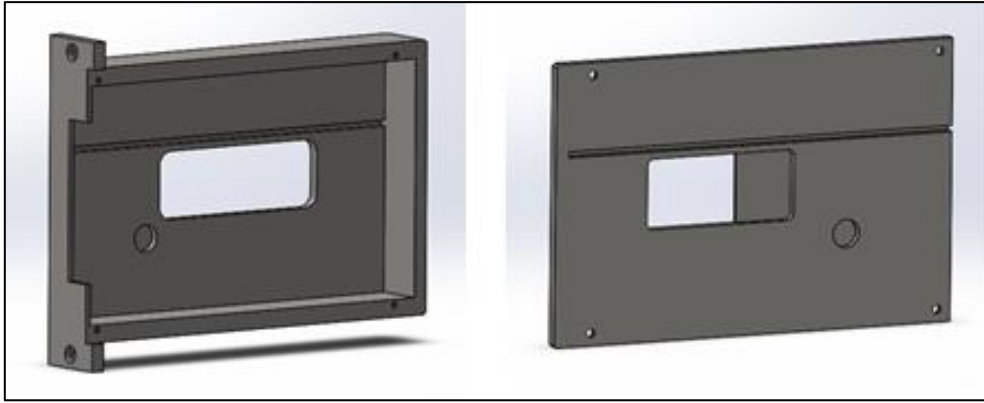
Tapa izquierda (izquierda) y Tapa derecha (derecha).
